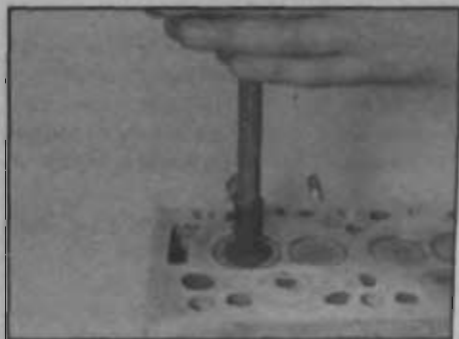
Притирка рабочей поверхности тарелки клапана
